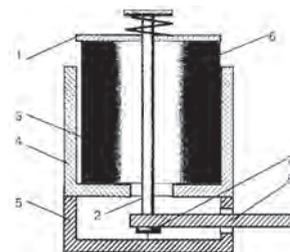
Конструктивная схема резинового виброизолятора подвешенного типа: 1–крышка; 2–стержень; 3–зазор; 4–кожух; 5–корпус; 6–резиновый упругий элемент; 7–головка стержня; 8–кронштейн для крепления к опорной поверхности станка.
